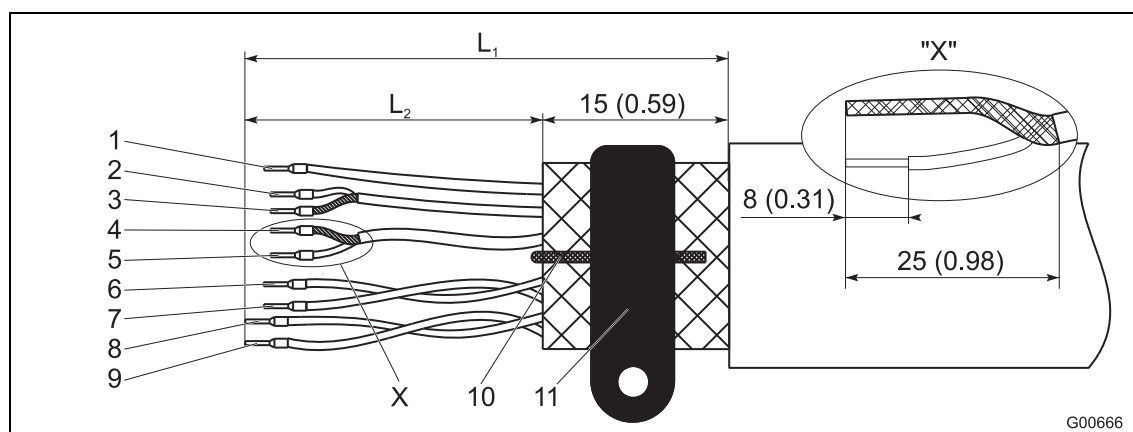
Côté transmetteur, dimensions en mm (inch)
